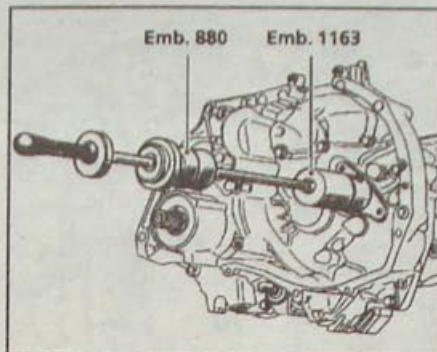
Использование съемника Emb. 880 и приспособления Emb. 1163 для снятия направляющей втулки подшипника выключения сцепления
